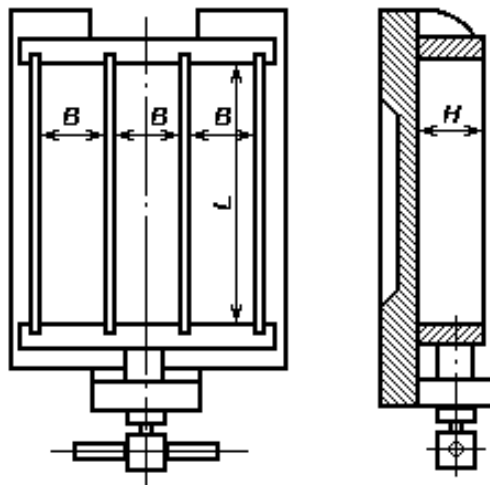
Форма для виготовлення зразків-балочок:
